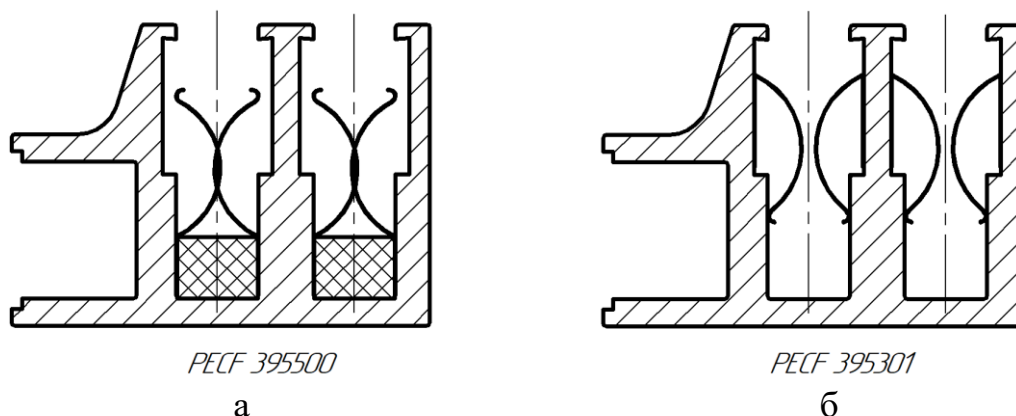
Схема установки контактно-металлических пружин: а) встречное; б) предлагаемое
